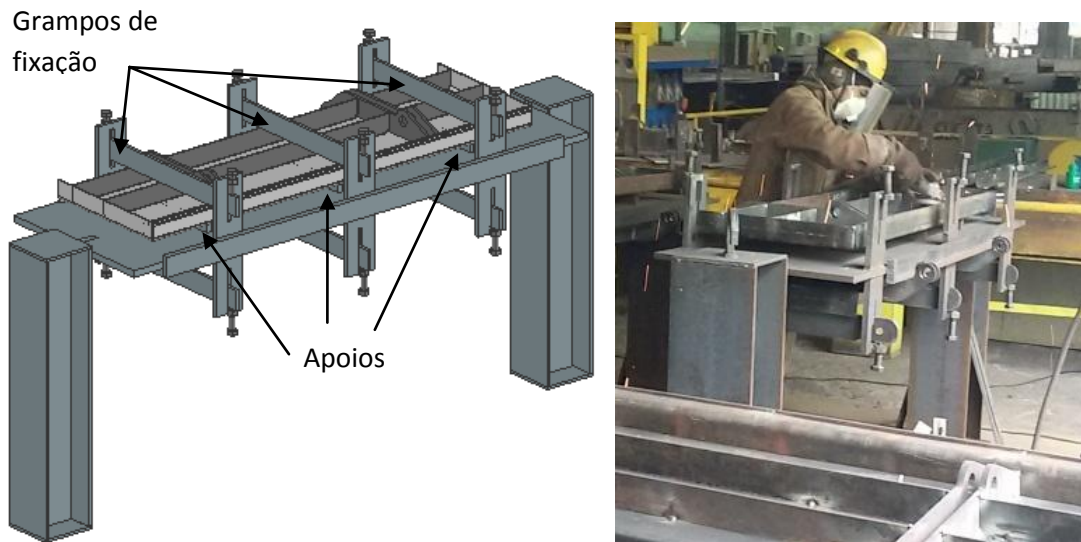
Dispositivo de fixação utilizado na fabricação da peça.
